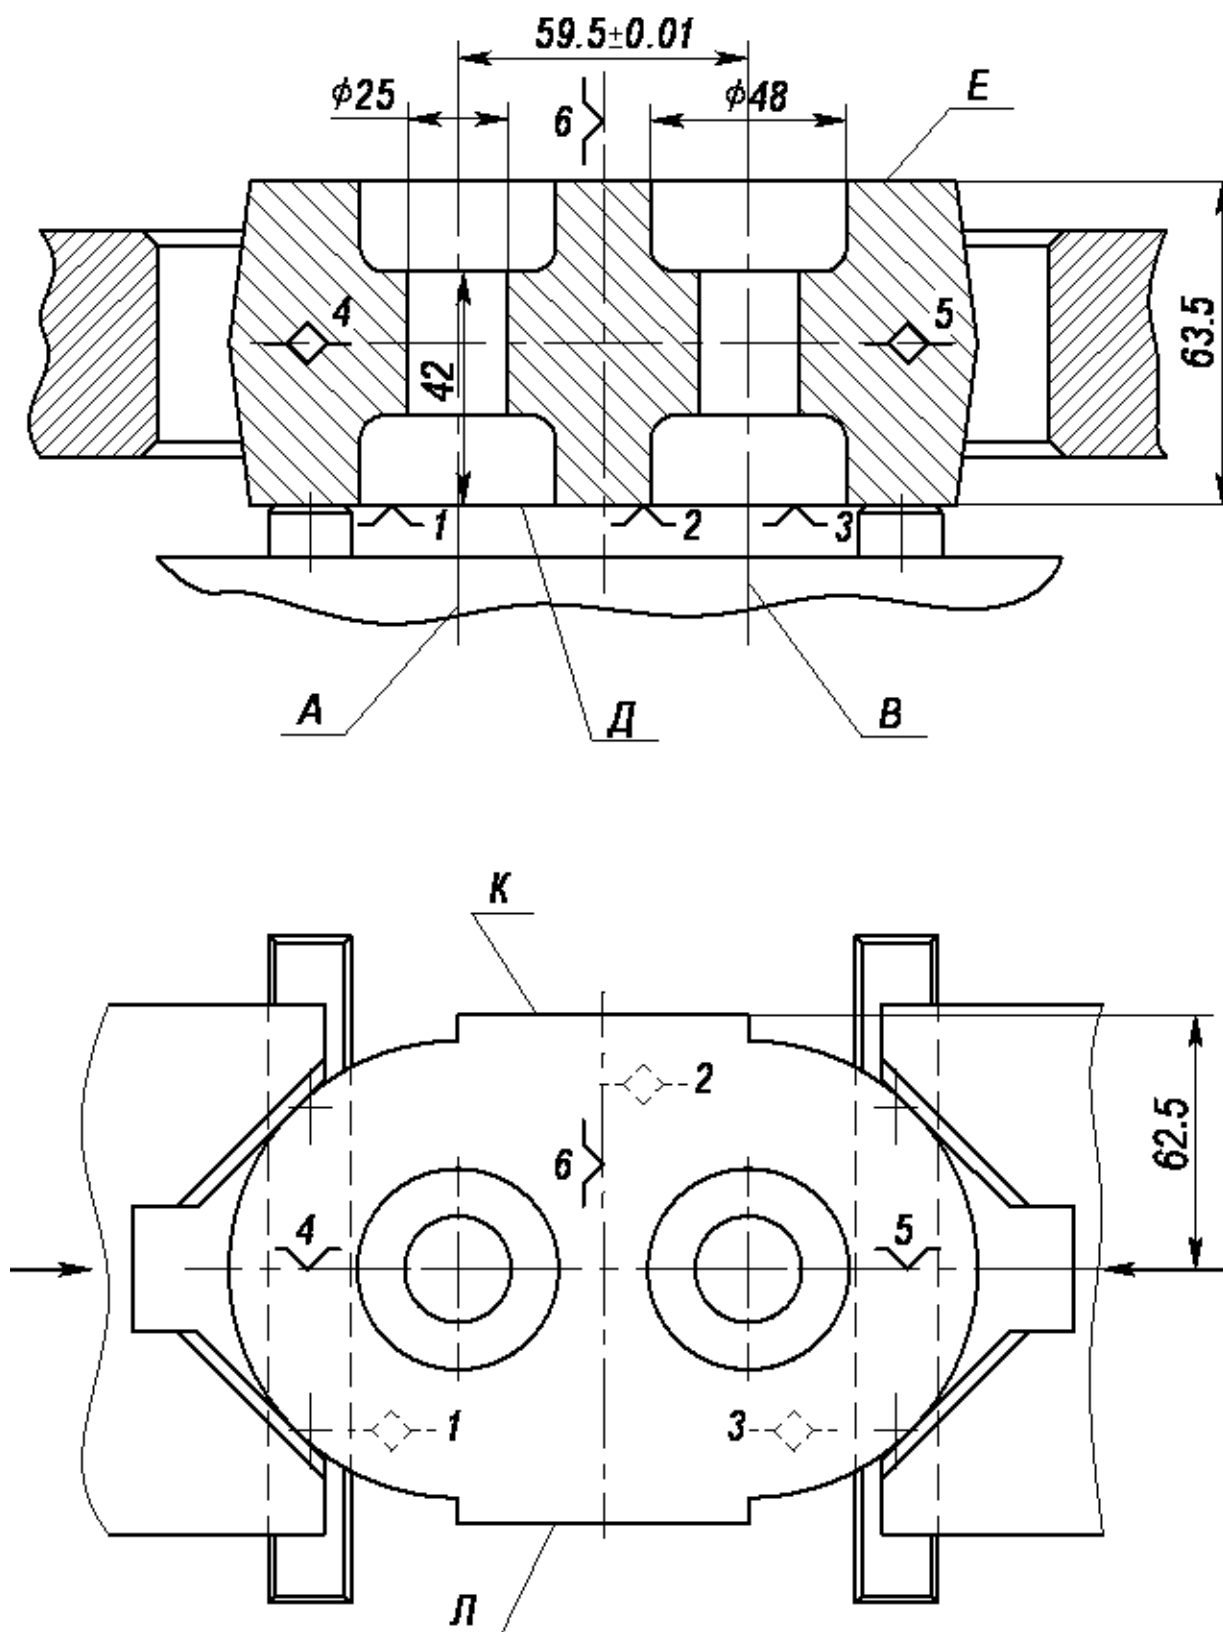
Схема базування корпусу по необроблених поверхнях (на перших операціях)
